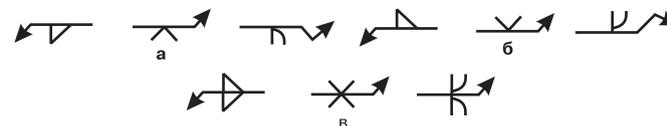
Символы, обозначающие сварку на подкладке.
